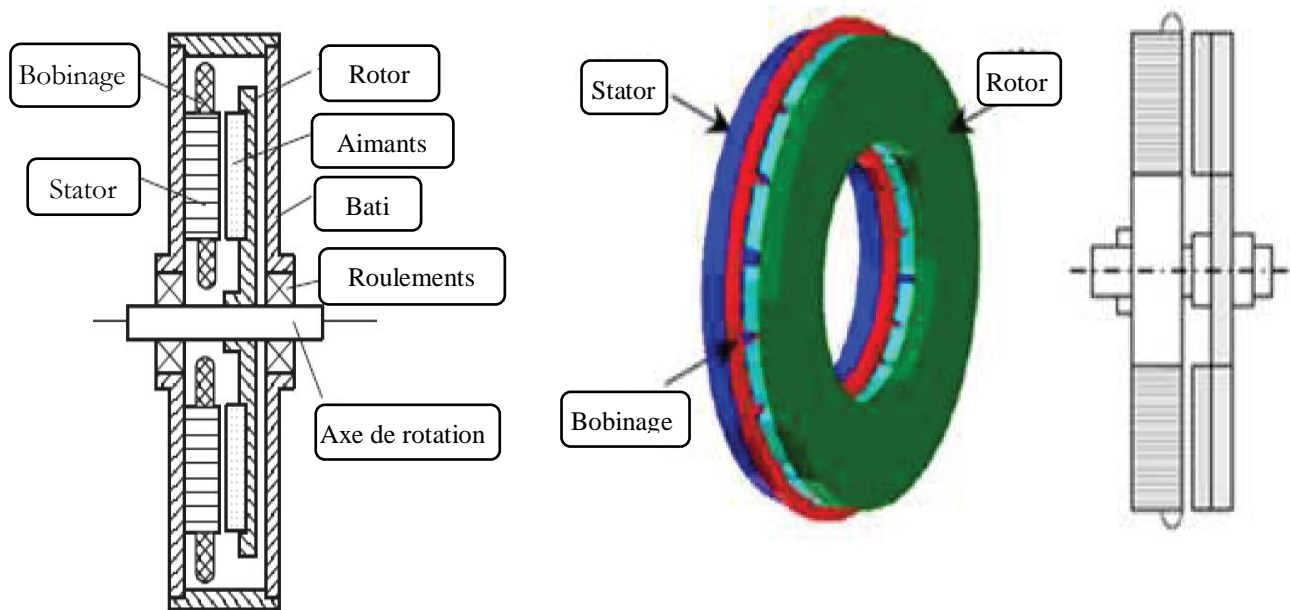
Descriptif de la Machine à Flux Axial 1 Stator / 1 Rotor, [8].
